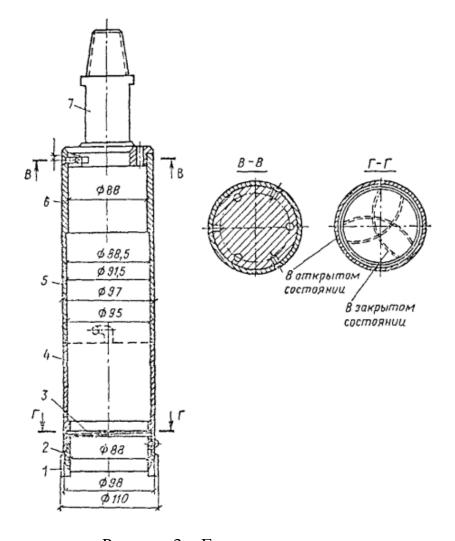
Грунтонос 1-тормозная лопасть; 2-башмак; 3-лепесток; 4-нижний стакан; 5-гильза; 6-верхний стакан; 7-головка
